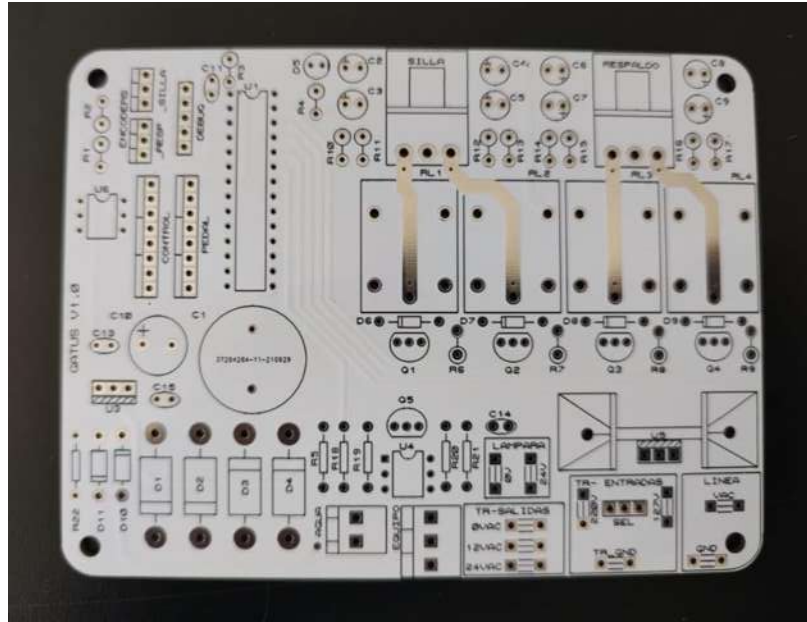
DISEÑO DE PCB PARTE DELANTERA
